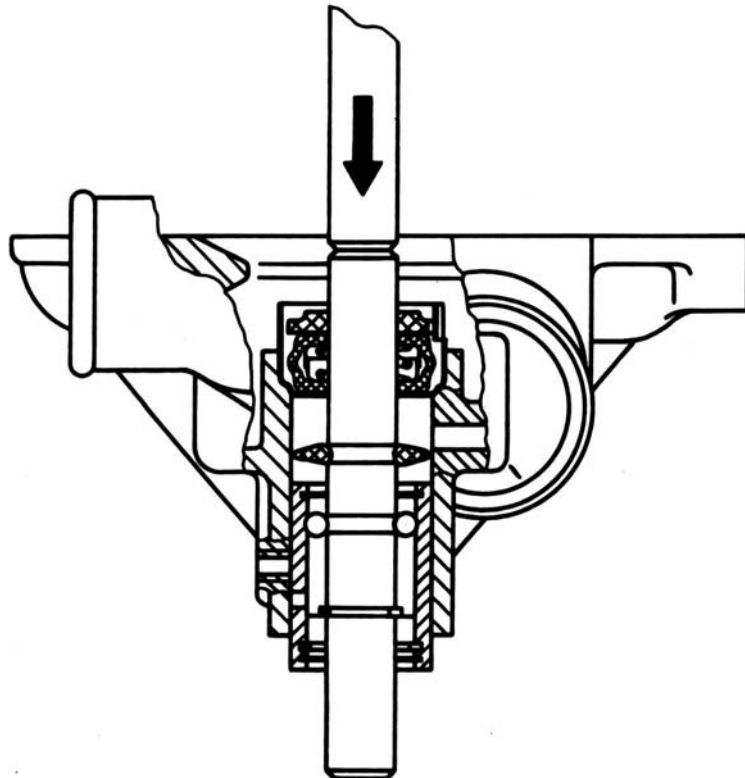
Выпрессовка подшипника с валиком насоса
